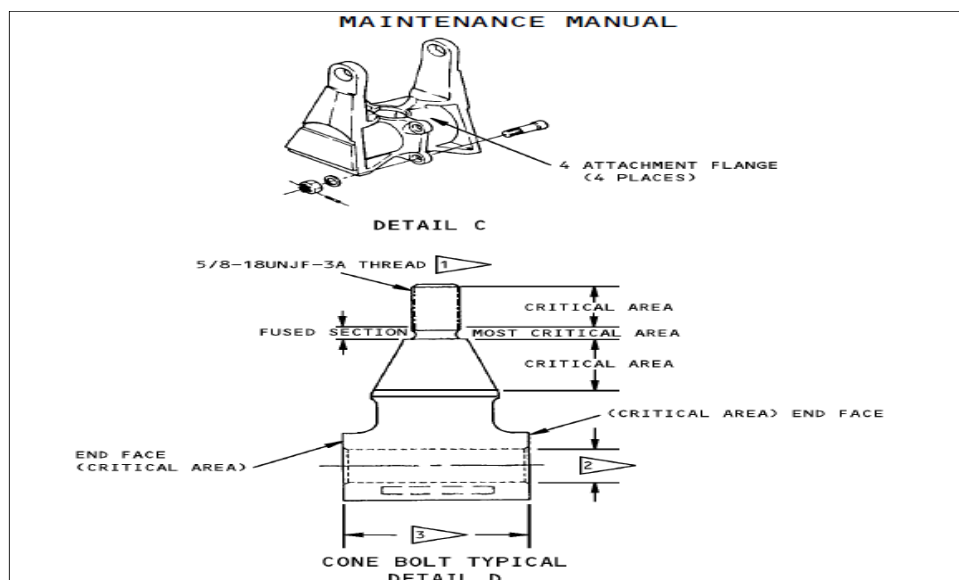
Detalle del pin de soporte "CONE BOLT y FLANGE"
